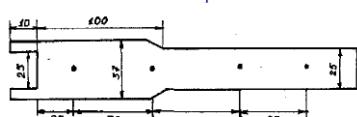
Шаблон для сверления отверстий в боковой планке гнездовых рамок
